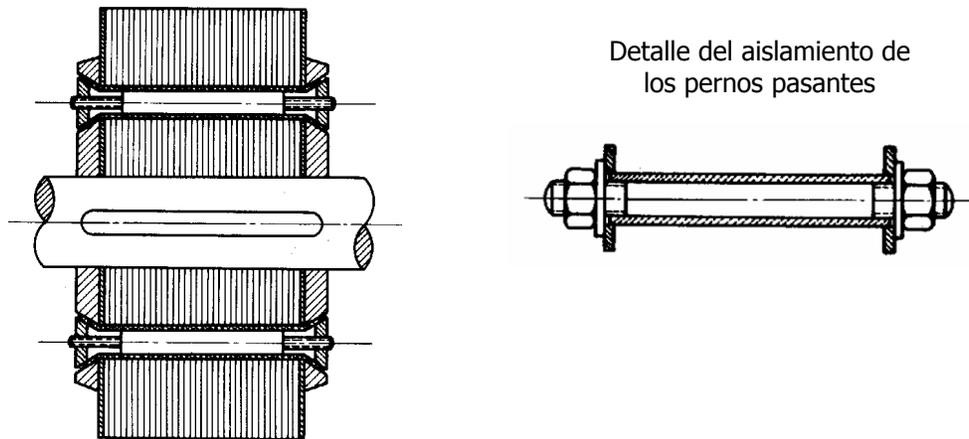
Paquete de chapas del rotor , utilizando el propio eje.
